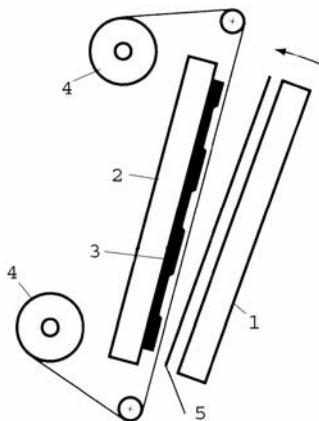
Позолотный пресс с качающимся тиглем: *1* — качающаяся плита (тигель); *2* — неподвижная плита (талер); *3* — штамп; *4* — фольговое устройство (аппарат); *5* — лист
